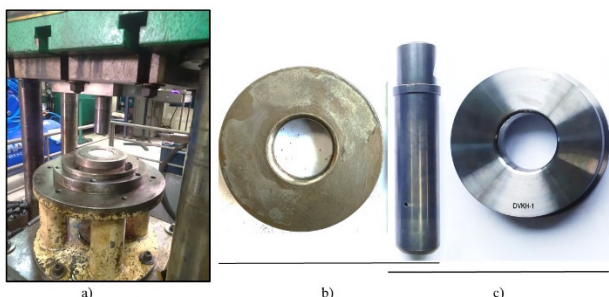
Матрица и инструментальная оснастка для комбинированного процесса глубокой вытяжки
